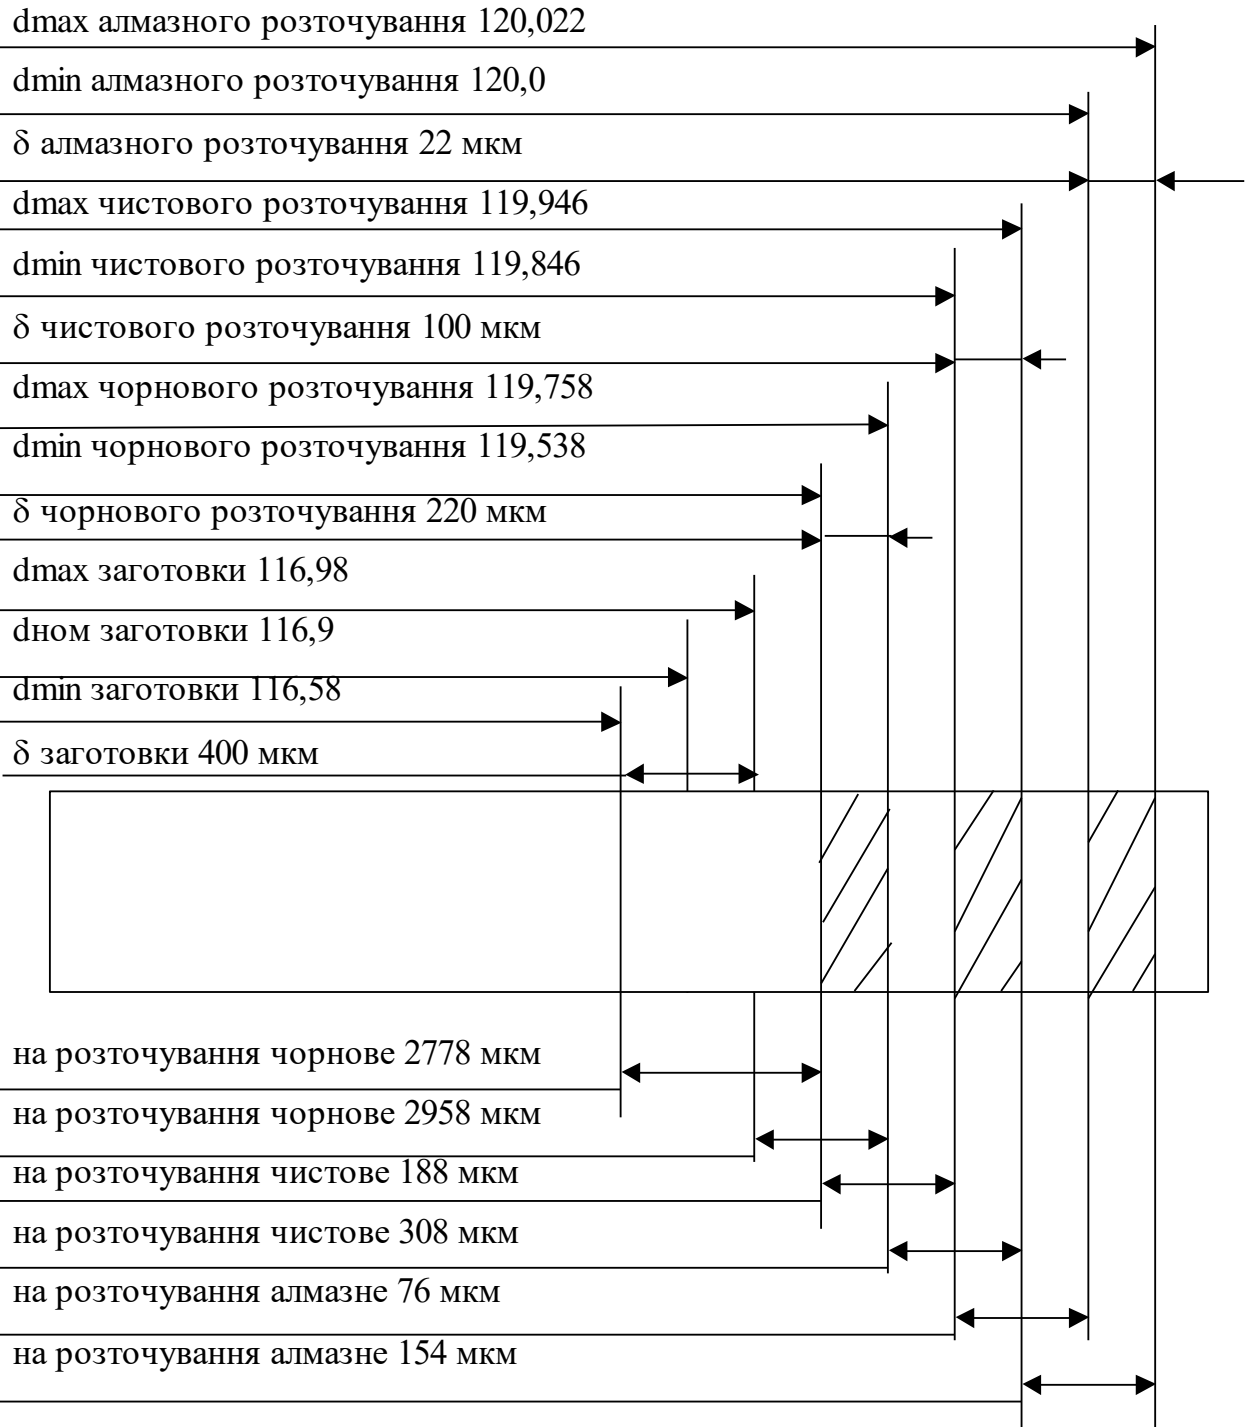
Схема розташовування припусків і допусків на обробку  $\varnothing 120^{+0.022}$
